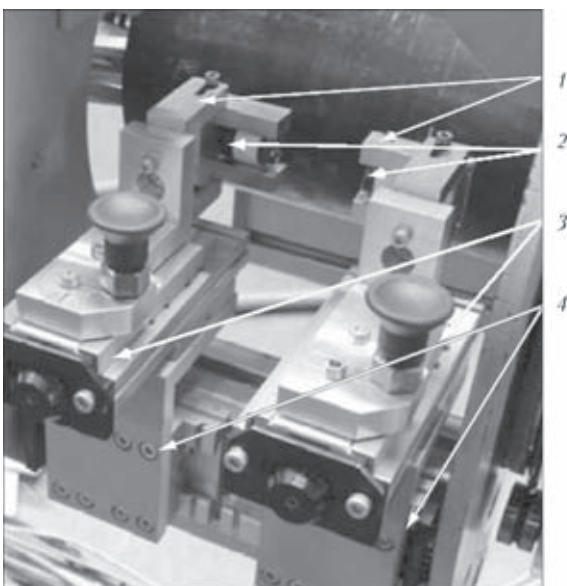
Устройство для ультразвукового контроля: 1 — зажимное устройство для ультразвуковых зондов; 2 — ультразвуковые роликовые зонды; 3 — оси для грубой регулировки по высоте; 4 — оси для регулировки расстояния до сварного соединения
